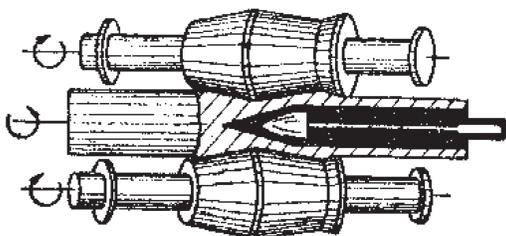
Прошивка на прошивных станках с косо расположенными валками
